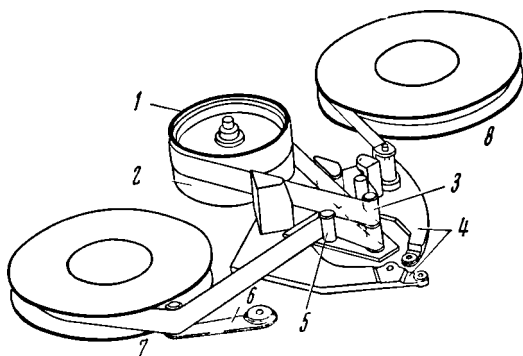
Лентопротяжный механизм комбинированного типа: 1 — вращающийся верхний барабан; 2 — неподвижный нижний барабан; 3 — ведущий вал; 4 — направляющие стойки; 5 — направляющий ролик; 6 — натяжной рычаг; 7 — подающая катушка; 8 — принимающая катушка
